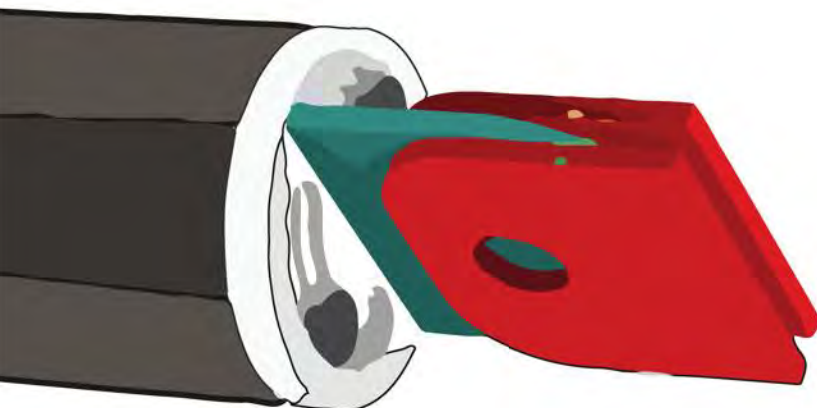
Dibujo tecnico de despiece del Brazo Adaptabletable.
